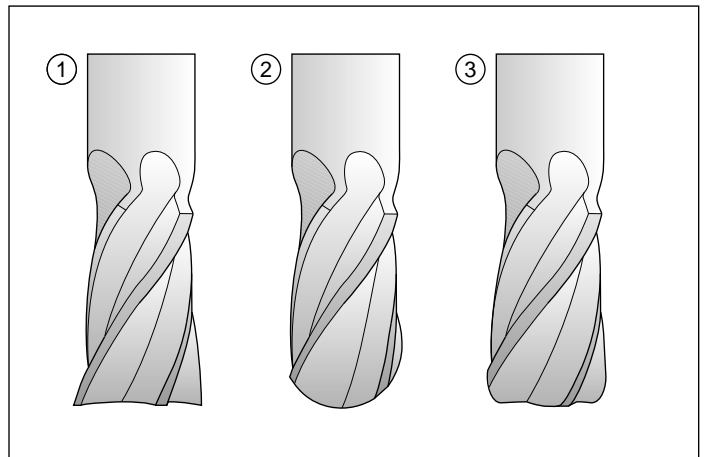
Werkzeugformen bei der 3D-Korrektur: Schaftfräser (1), Radiusfräser (2), Eckenradiusfräser (3)
